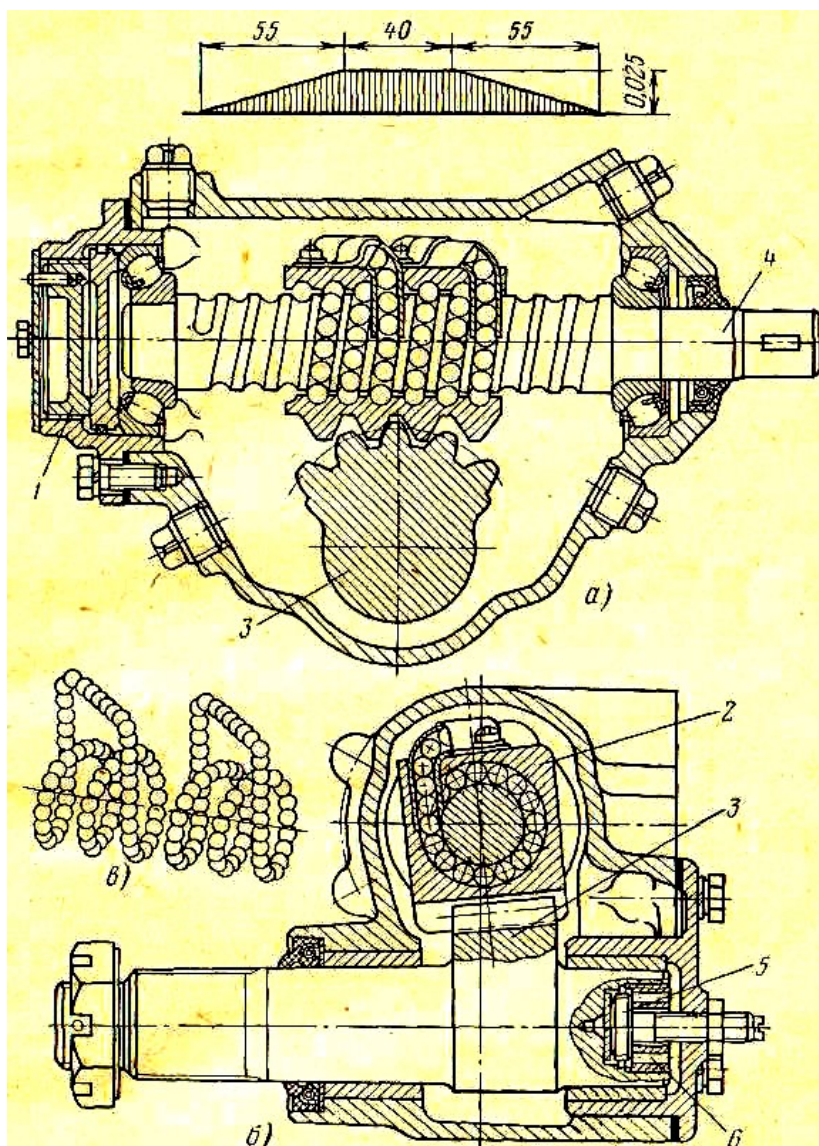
Рулевой механизм с винтовой передачей и зубчатой парой
